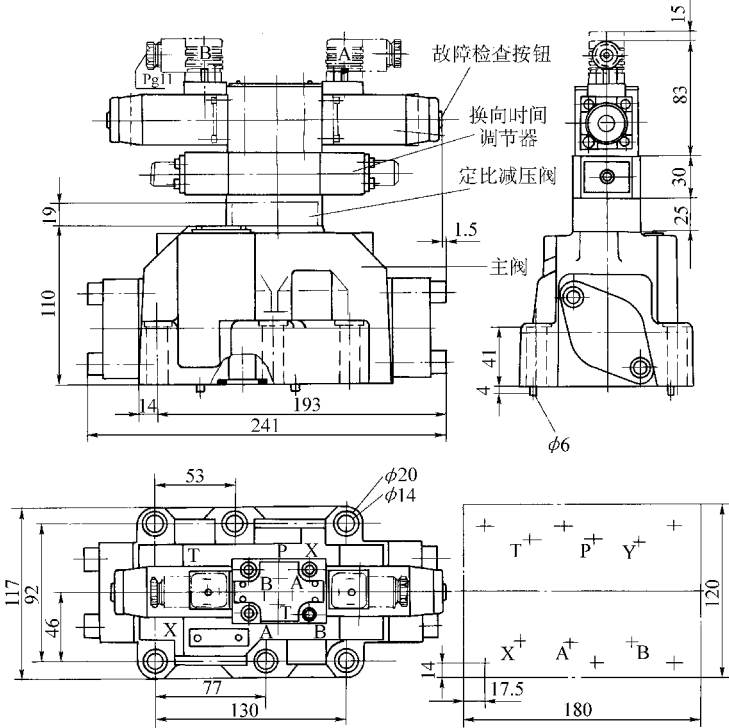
4WEH22 型电液换向阀外形尺寸
